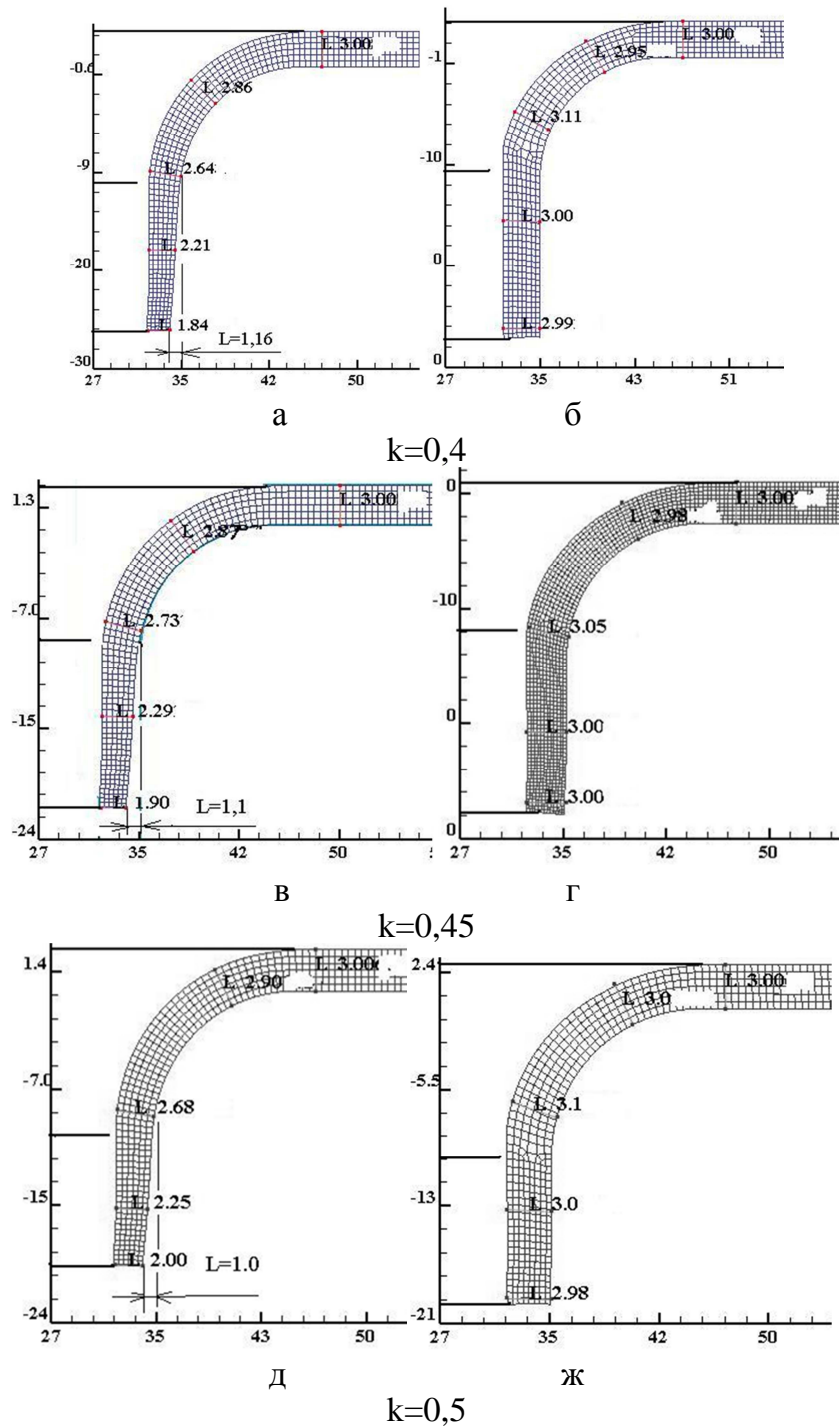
Розміри L (мм) zdeформованих частин заготовок, які отримані відбортуванням традиційної заготовки (а, в, д) та зпрофільованої заготовки (б, г, ж) з коефіцієнтами відбортування 0,4; 0,45; 0,5
